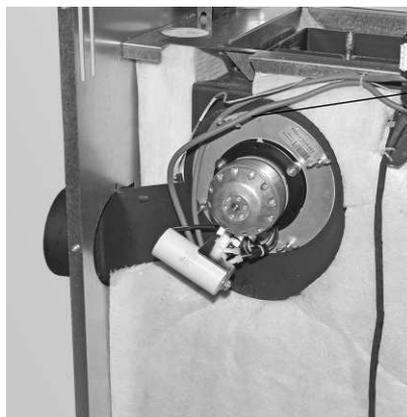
Riavvitare il ventilatore gas combusti ruotato di 90°
